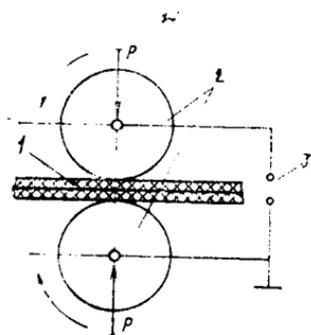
Схема сварки листовых термопластов токами высокой частоты
